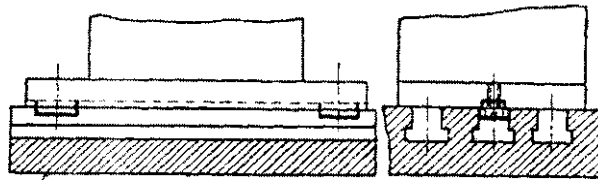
Схема ориентирования приспособления на столе станка с помощью шпонок, закрепленных на корпусе
